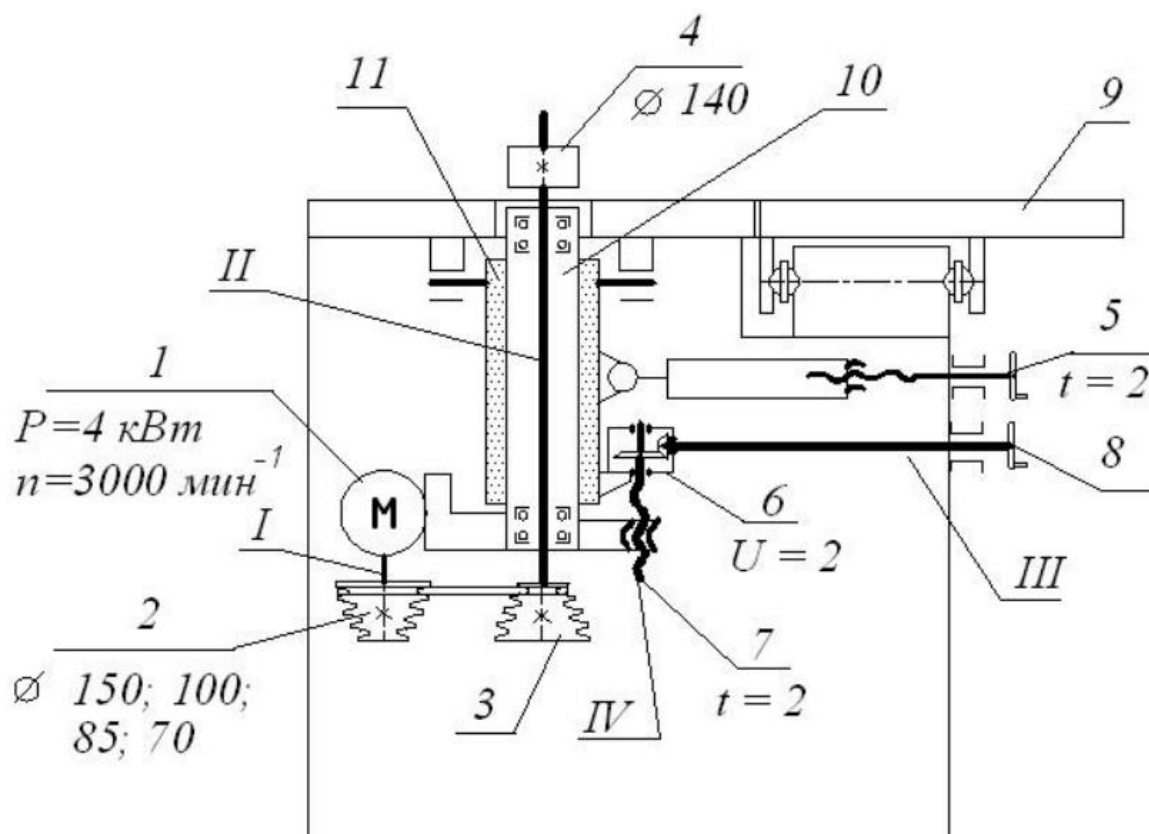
Фрезерный станок модели T1000 L с шипорезной кареткой
